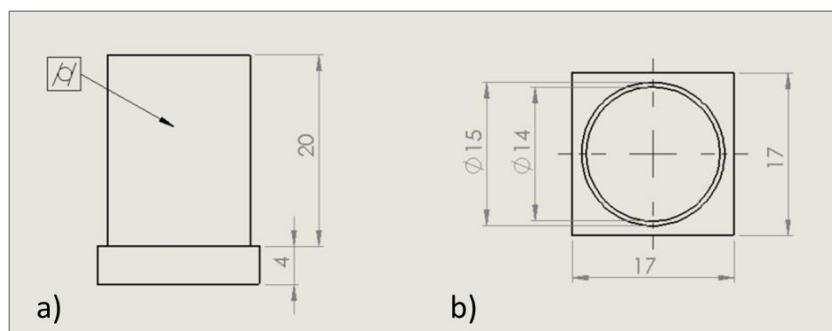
Dessin technique du tube, avec mesure de cylindricité a) vu de côté ; b) vu du dessus, en mm
